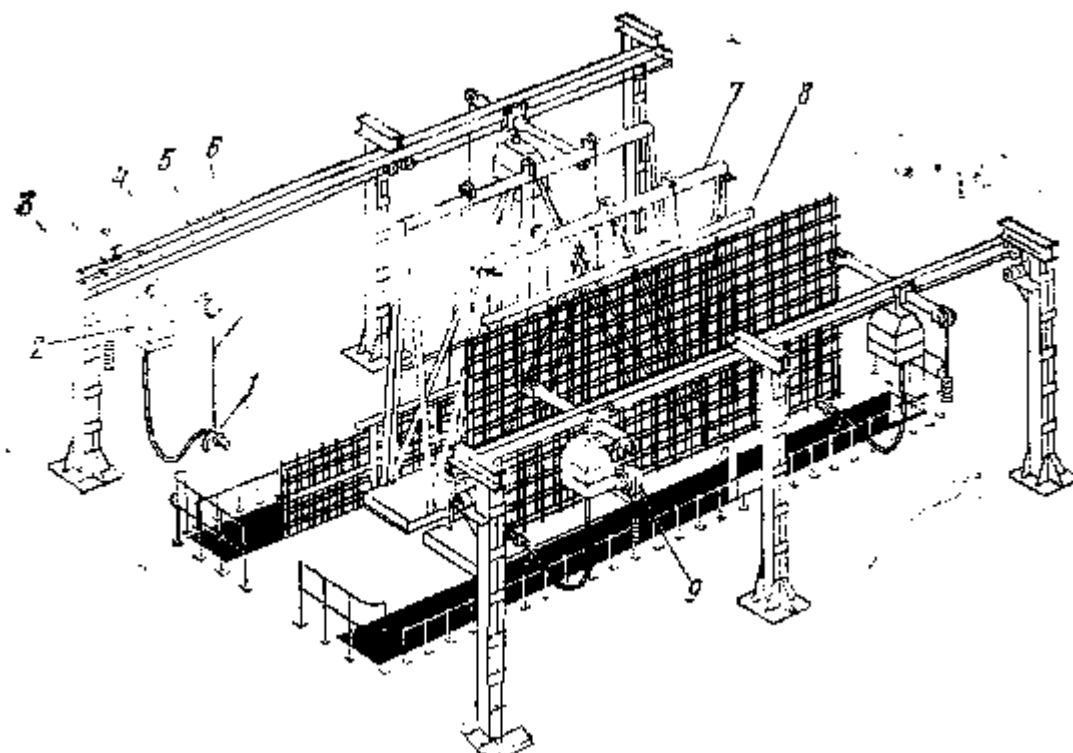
Вертикальная установка СМЖ-286А для сборки и сварки арматурных каркасов
